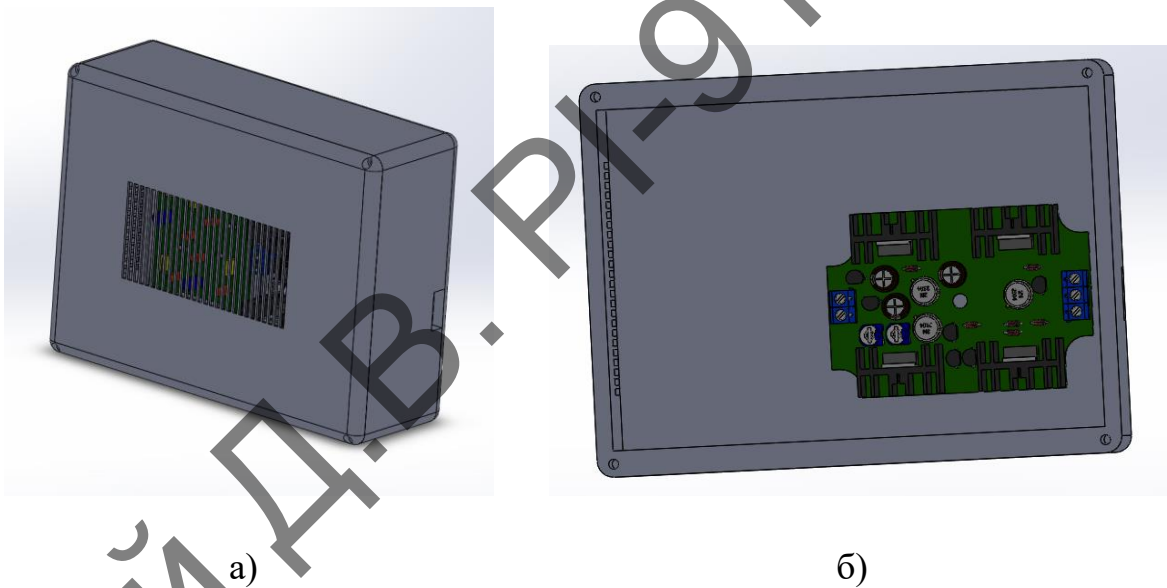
Корпус G758V (а) та підсилювач (б)
